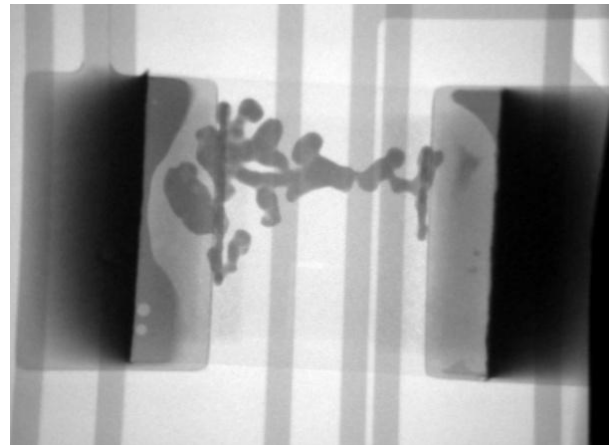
Příklady defektu solder graping – převzato z [29, 30]
